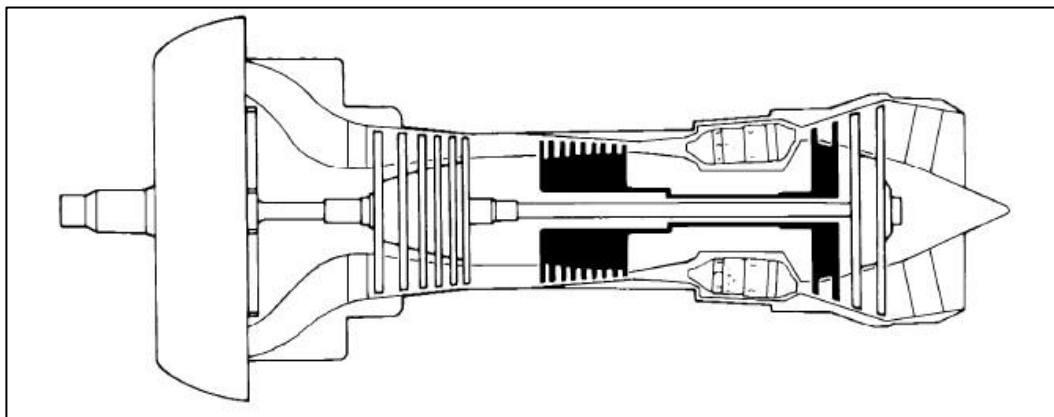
Turbohélíce de compresor de dos etapas y flujo axial [5]
